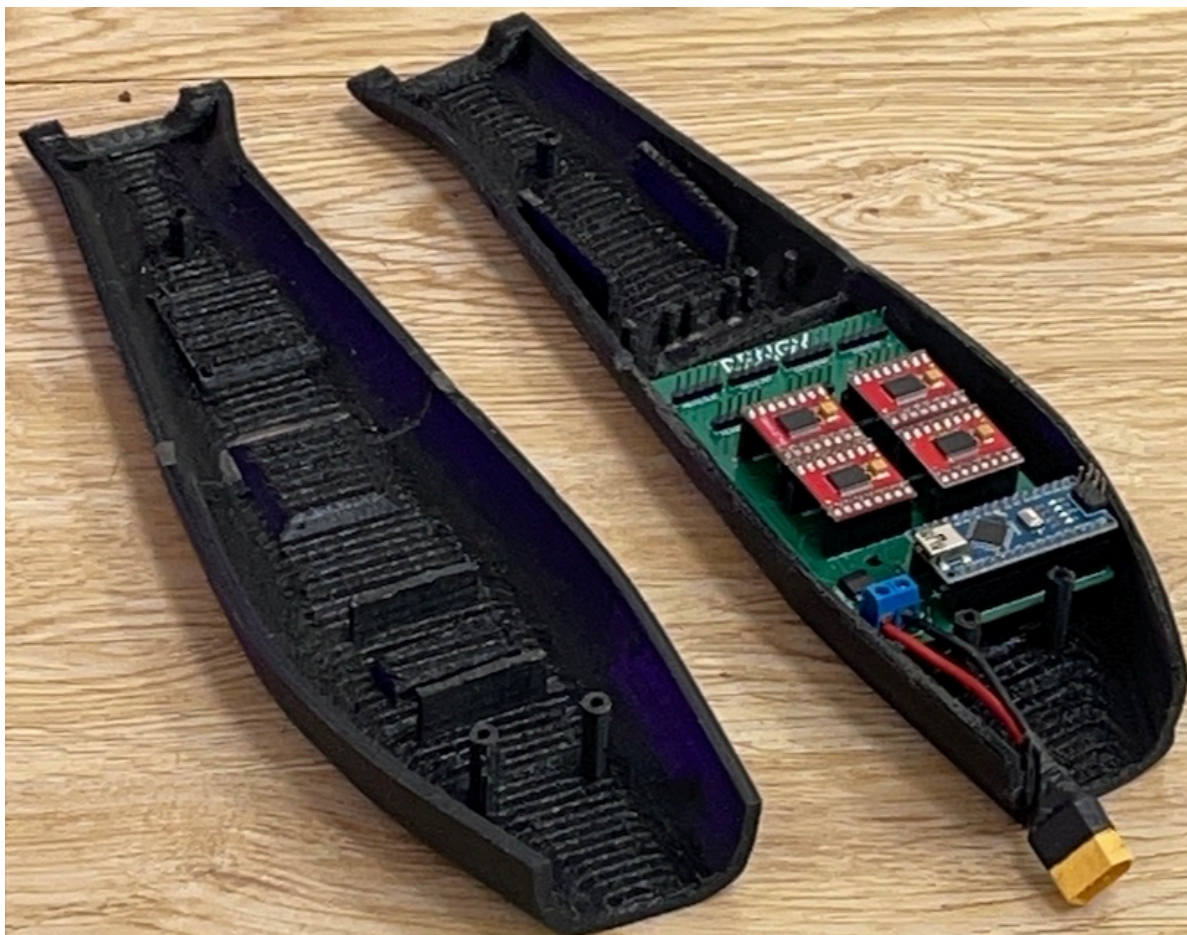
Prueba de posicionamiento de la placa de circuito impreso PCB.
